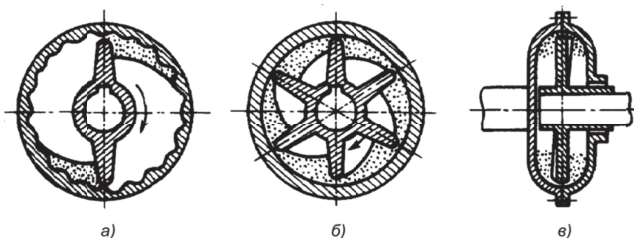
Схемы центробежных муфт со свободным твердым наполнителем
